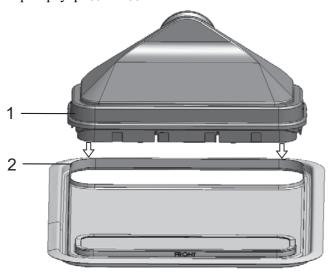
Установка воздушной коробки на крышку резервуара для воды
